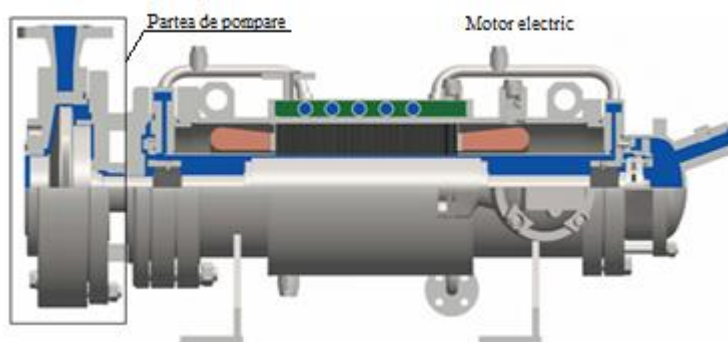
Pompa ermetică cu motor capsulat de tip CH (Secțiunea axială)
